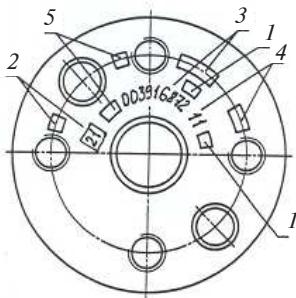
Клейма и знаки маркировки, относящиеся к изготовлению оси:
